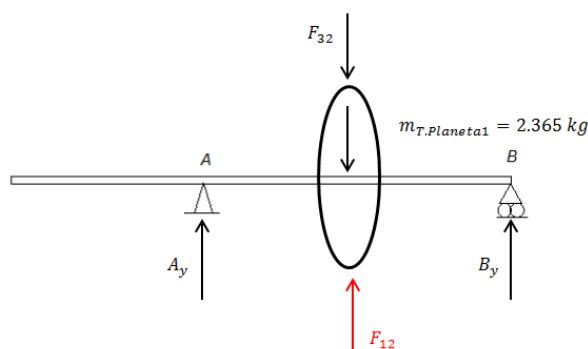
Esquema de fuerzas que actúan sobre el engranaje planeta
